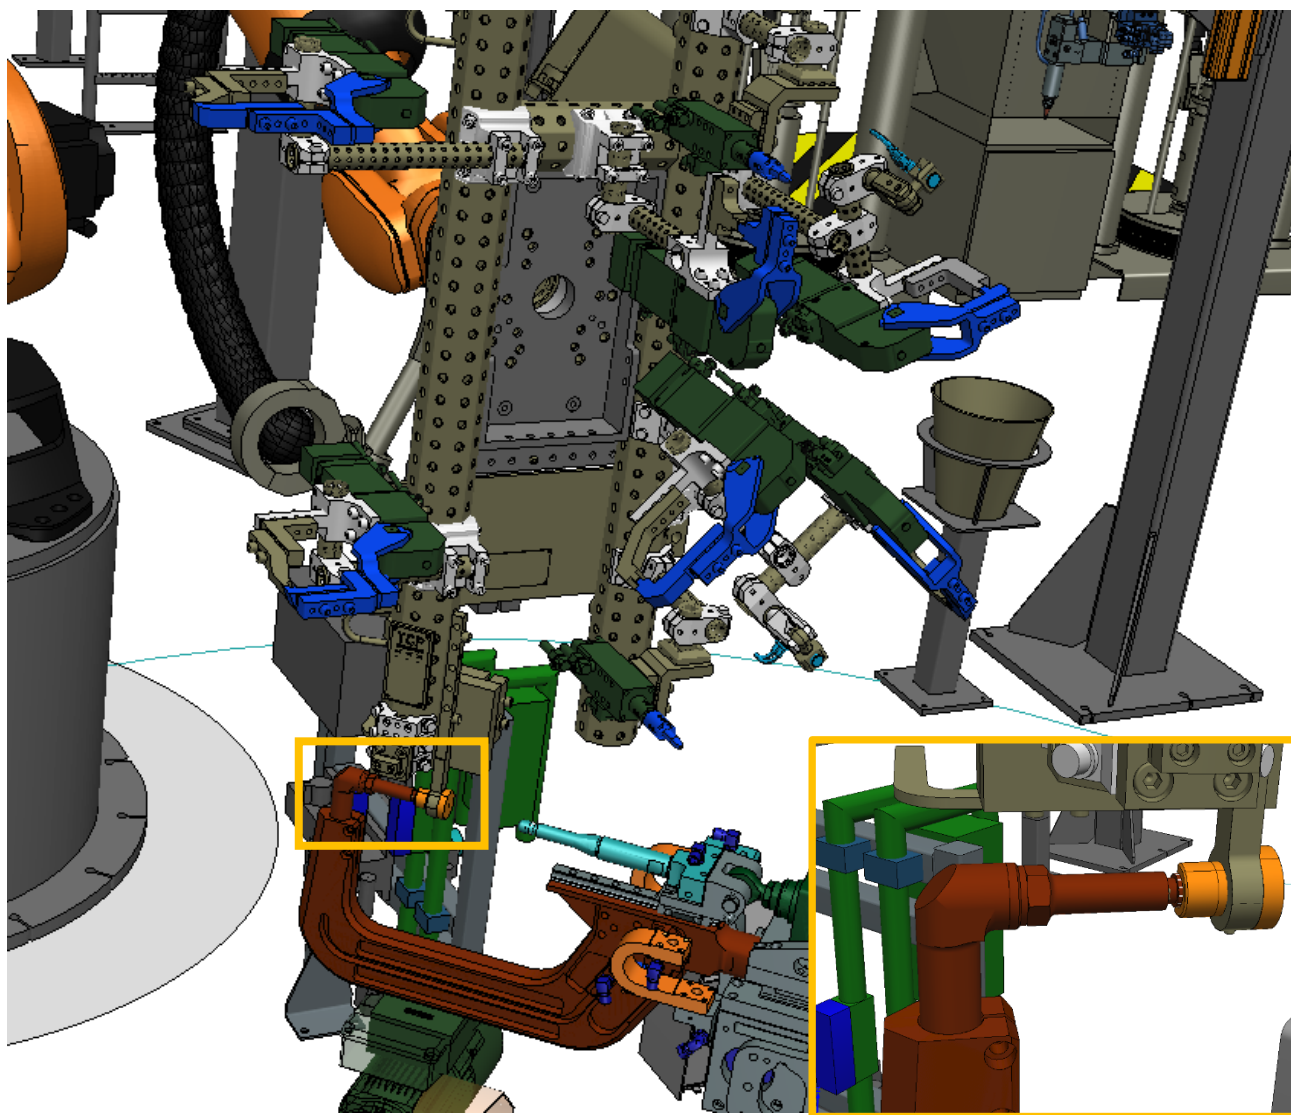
Калибровочное положение сварочного пистолета
